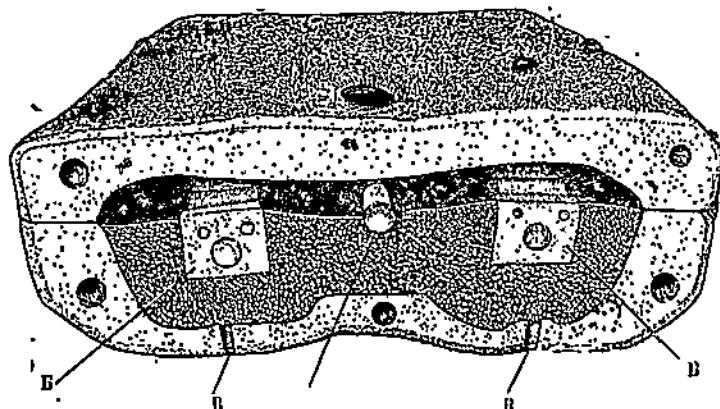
Изготовление клеевой формы для одновременной отливки „под давлением“ двух небольших бюстиков. Модели и кожухи, изготовленные для наливки передней половины формы. А — литник. Б — модели. В — отверстия между кожухом и плиткой для выхода воздуха при цаливке кляя. Для того, чтобы удержать клей в кожухе, открытая часть последнего закрывается плиткой.
